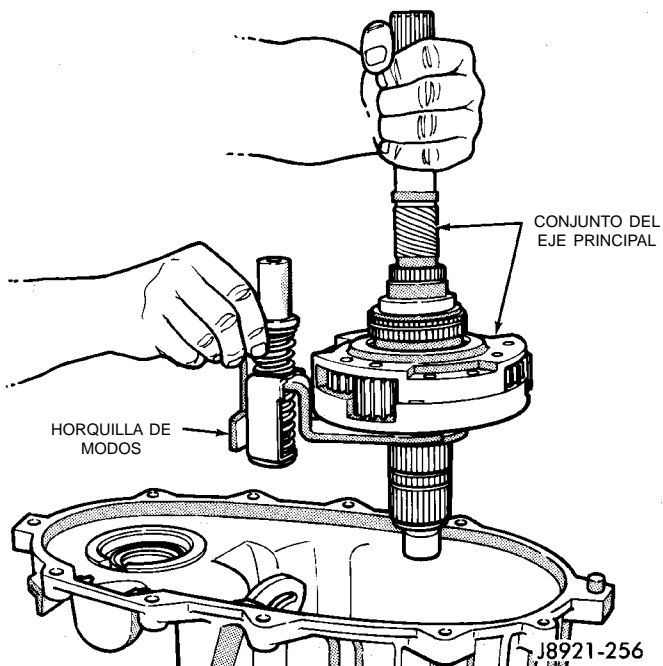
Instalación del eje principal y horquilla de modos ensamblados
